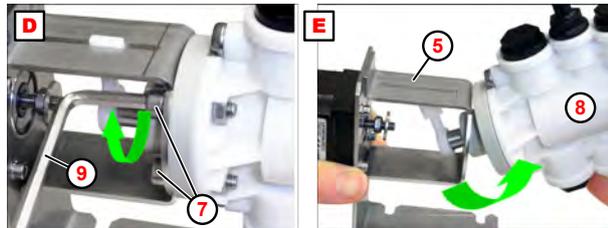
Vue générale de l'ensemble moteur/pompe
